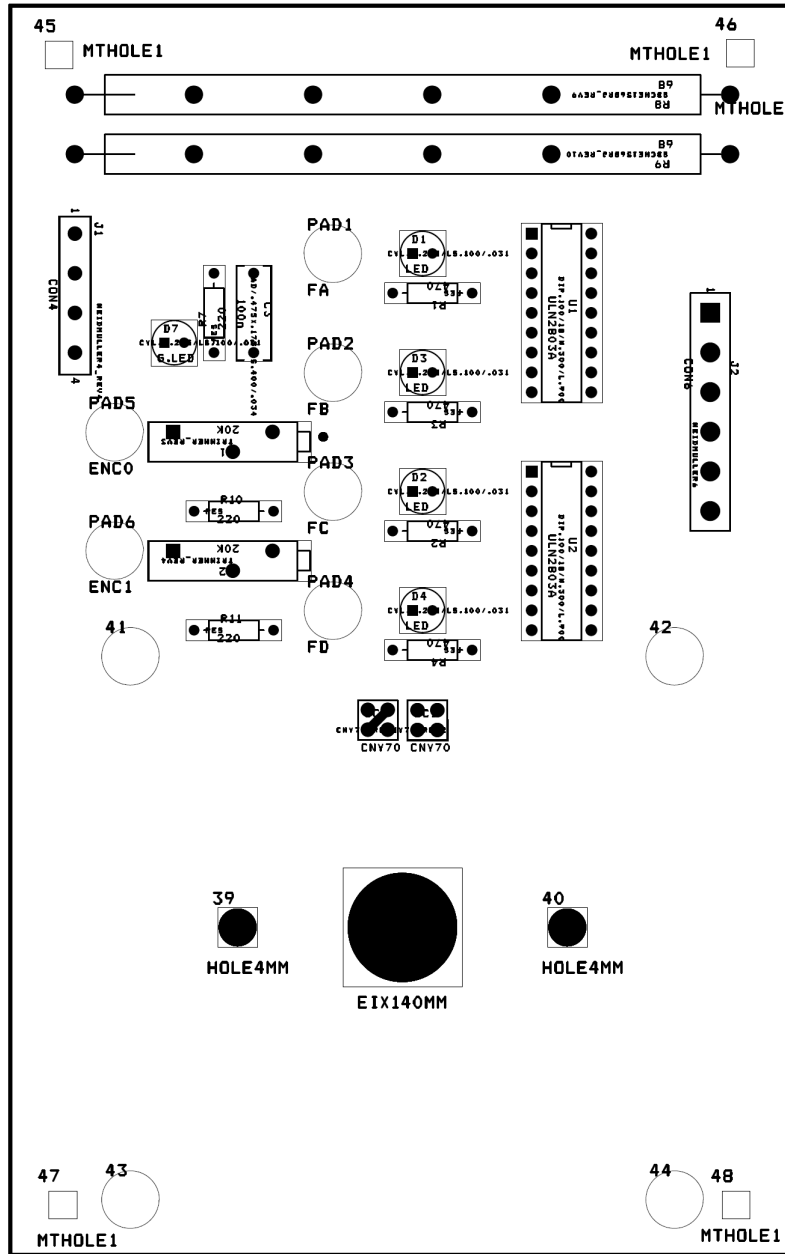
Capa d'acoblament (AST) de la PCB de la interfície per al motor unipolar
